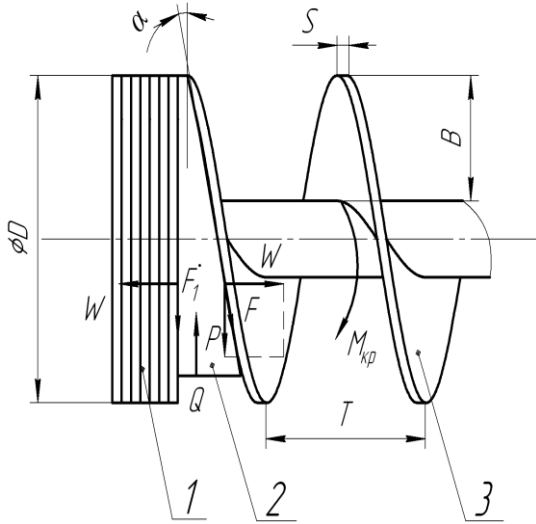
Расчетная схема приспособления для калибровки витка винтовой заготовки на шаг: 1 – плотно намотанная заготовка, 2 – клин; 3 – калиброванные витки винтовой заготовки
